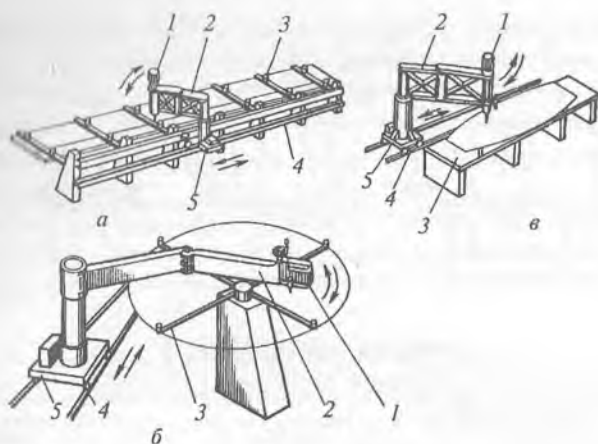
Сверлильно-зенковальные установки различных типов:
